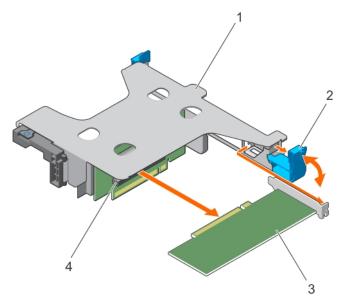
Retrait d'une carte d'extension mi-hauteur du module de carte de montage double
